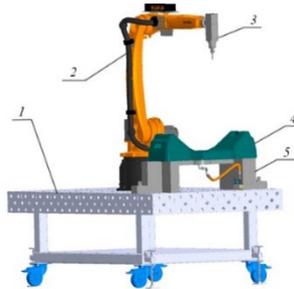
Модель роботизированной ячейки. 1 – сварочный стол, 2 – робот-манипулятор, 3 – инструмент с фрезой, 4 – обрабатываемая деталь, 5 – технологическая оснастка.
